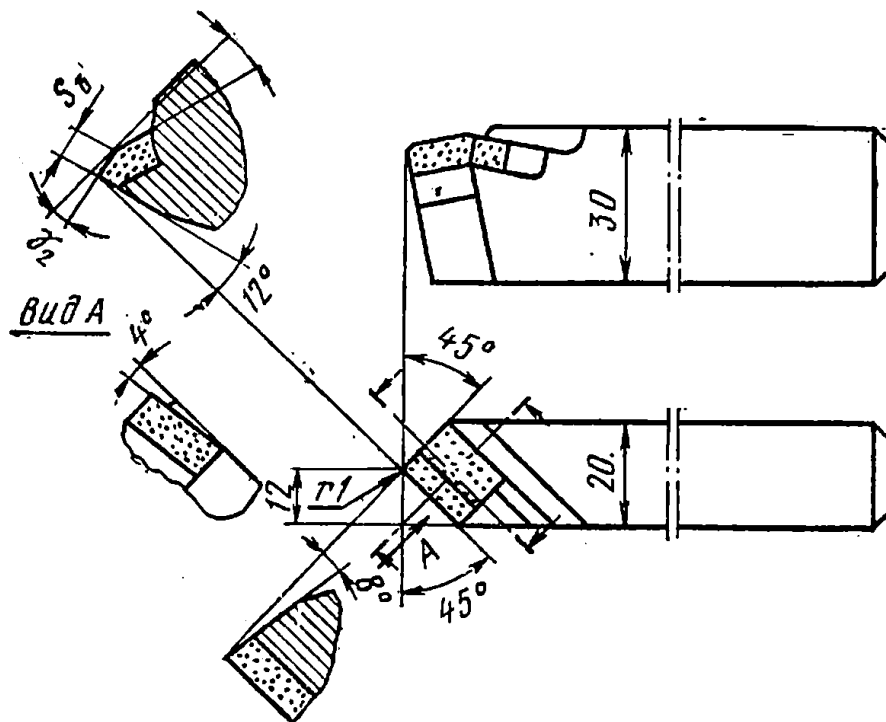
Геометрия режущей части резца для точения наплавленного металла. Для чернового точения $\gamma_2 = -15^\circ$, для чистового $\gamma_2 = -10^\circ$.
